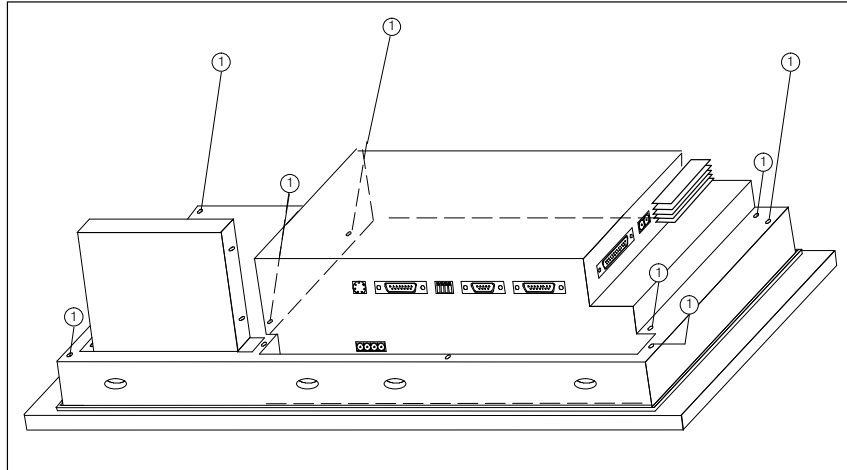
Schrauben der äußeren Gehäuserückwand lösen
